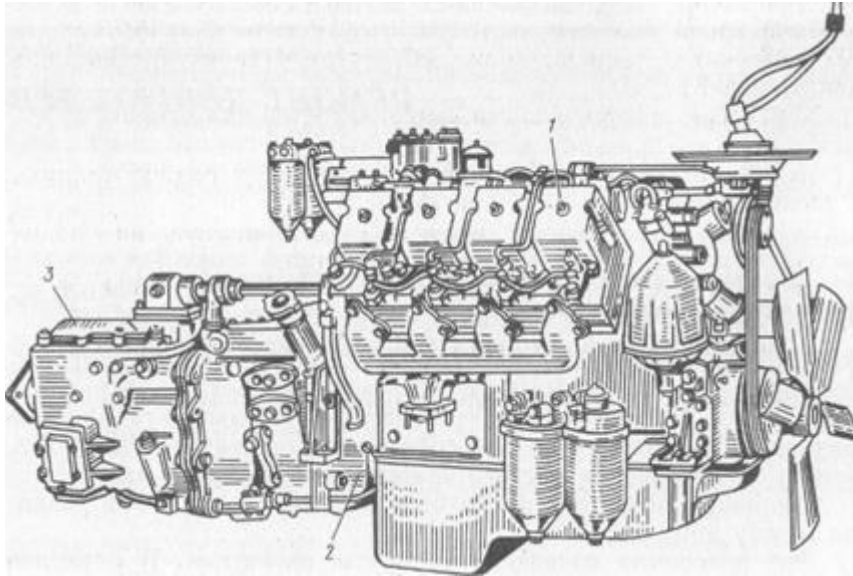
Загальний вигляд силового агрегату КамАЗ-740:
